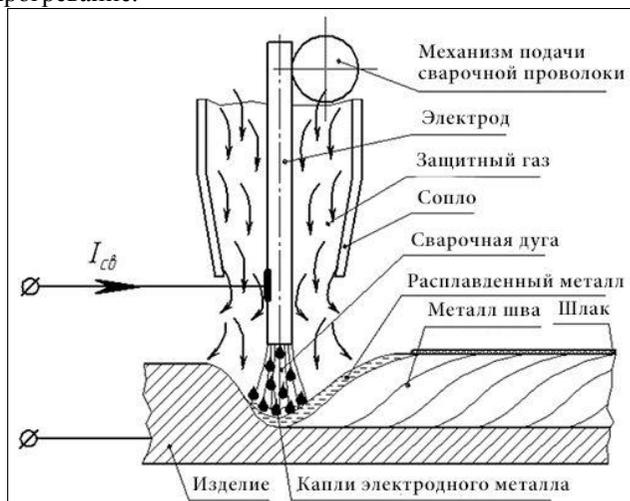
Схема сварки в среде защитных газов
